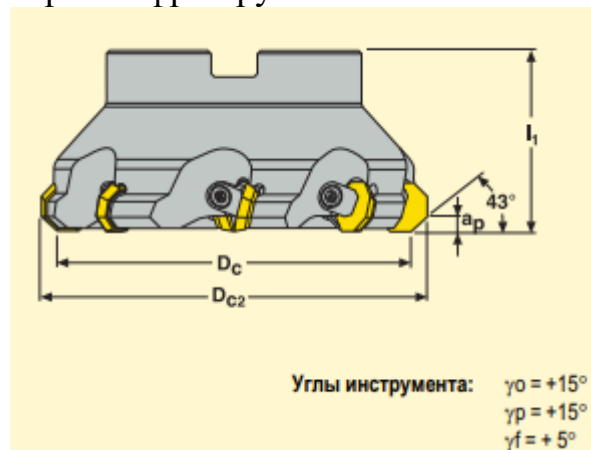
Фреза R220.43 -0050-07W [3, с.47]
